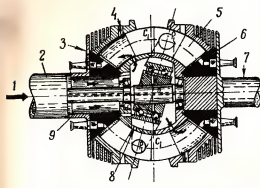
Продольный разрез двигателя 1 — входной топливный; 2 — стационарный блок; 3 — выход отработавших газов; 4 — поршень в одном из своих конических положений; 5 — выходной (верховый) вал; 6 — выходной (верховый) вал; 7 — выходной вал; 8 — уплотнение; 9 — уплотнение.
